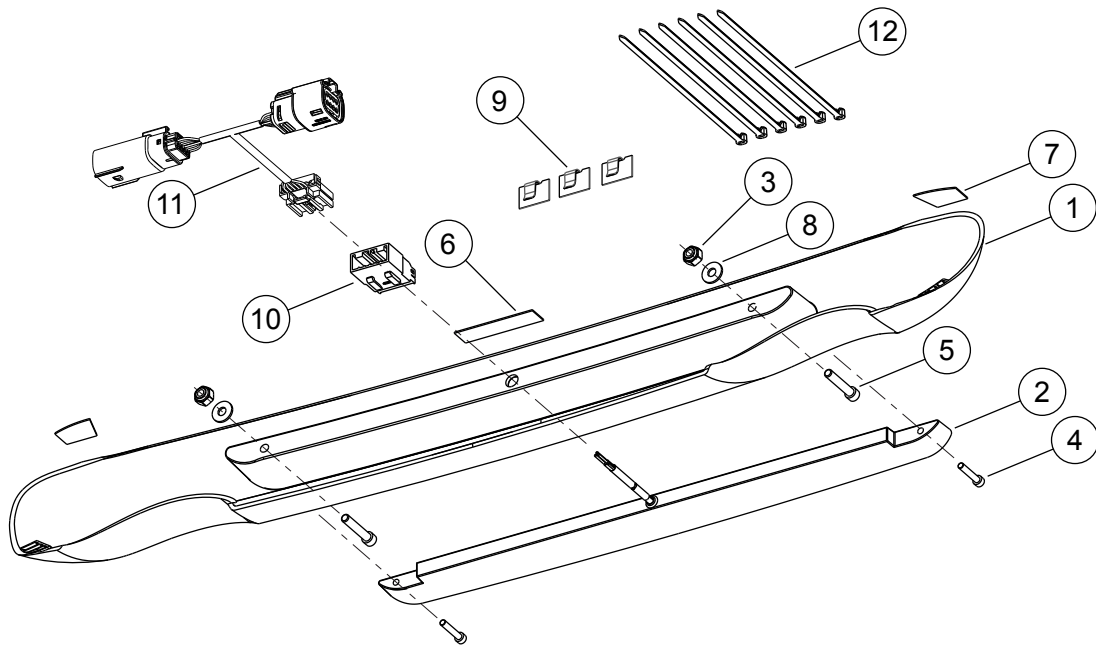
Pièces de rechange : Feu arrière additionnel TRIGLIDE
